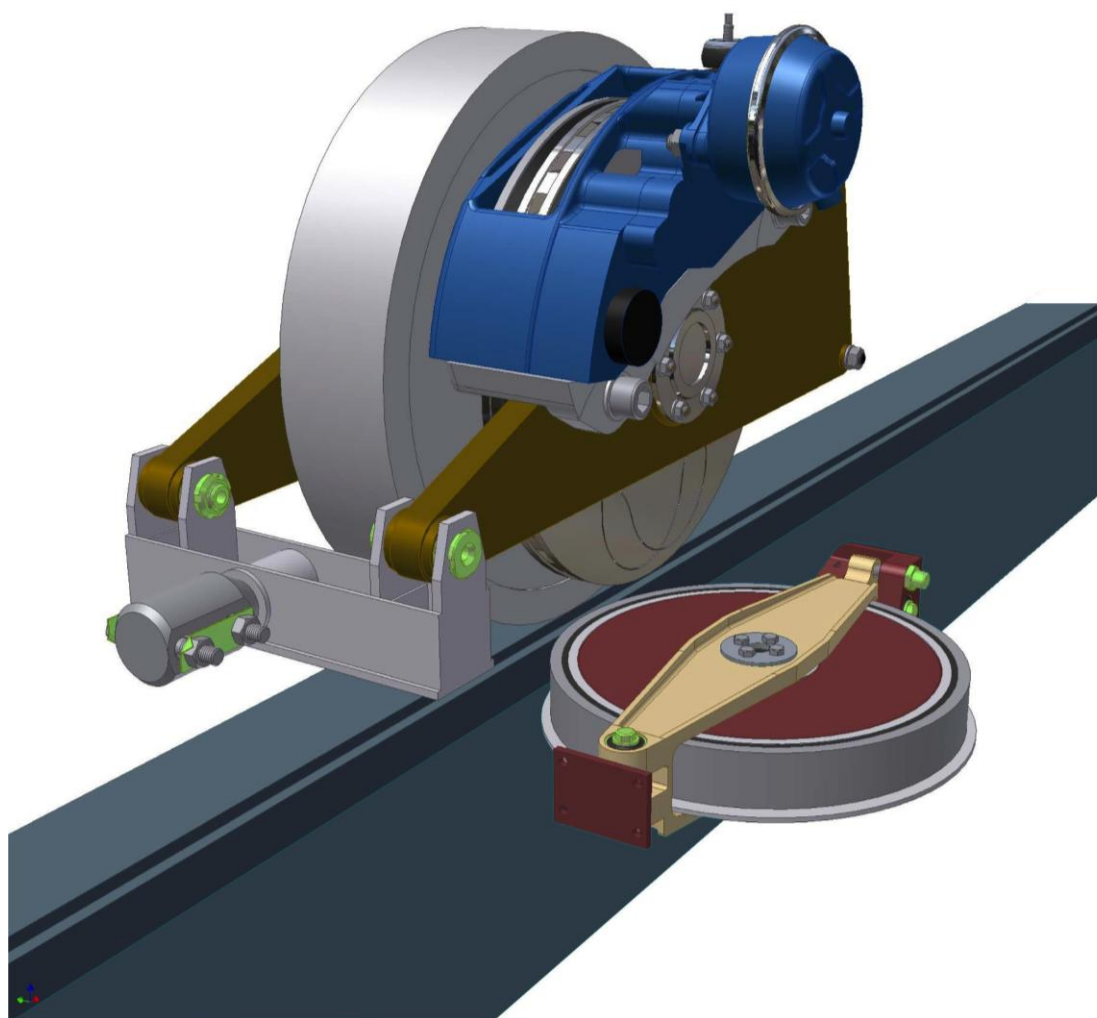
Общий вид опорного колеса и противосходного бокового ролика юнибуса
